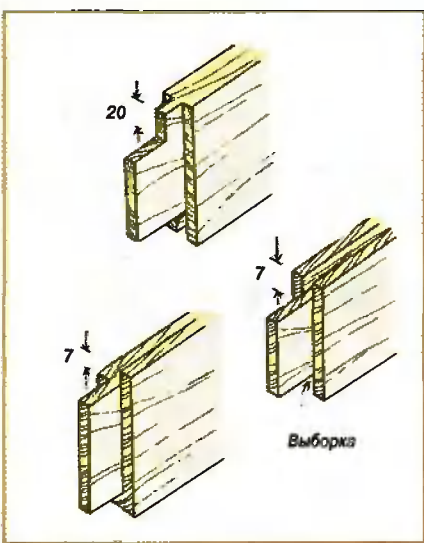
Форма шипов и верхних кромок поперечин С, D, E.
